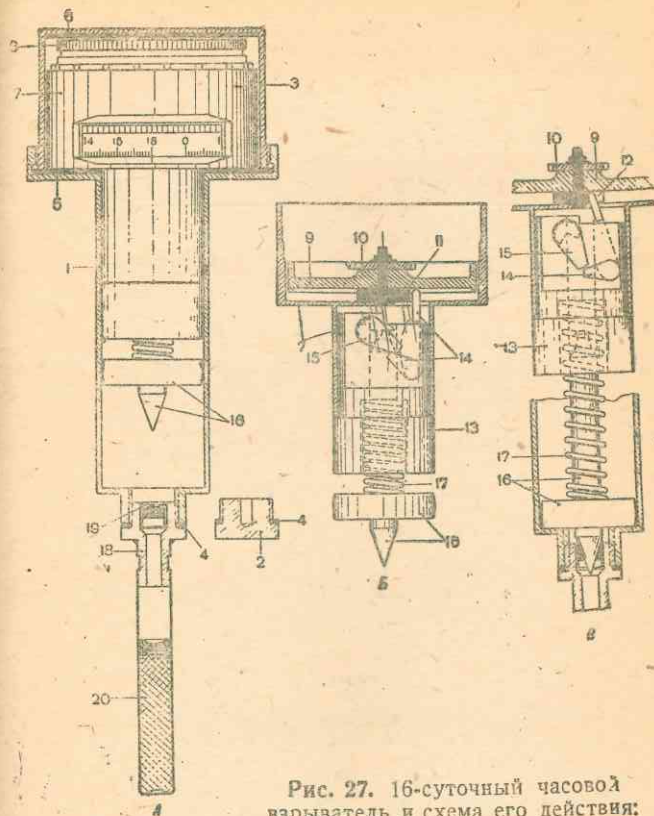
16-суточный часовой взрыватель и схема его действия:
